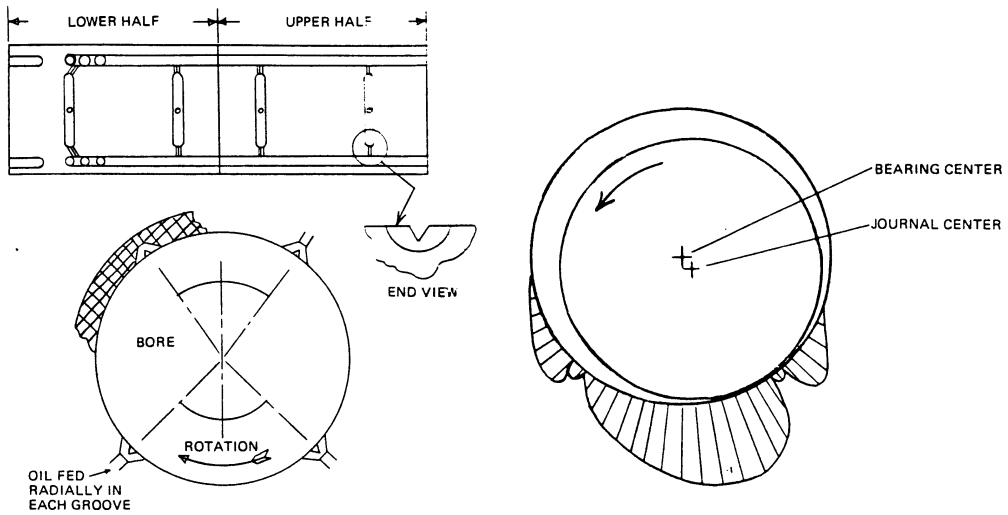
Axial Groove Bearing 그림 1-10 Axial Groove Bearing의 압력분포
